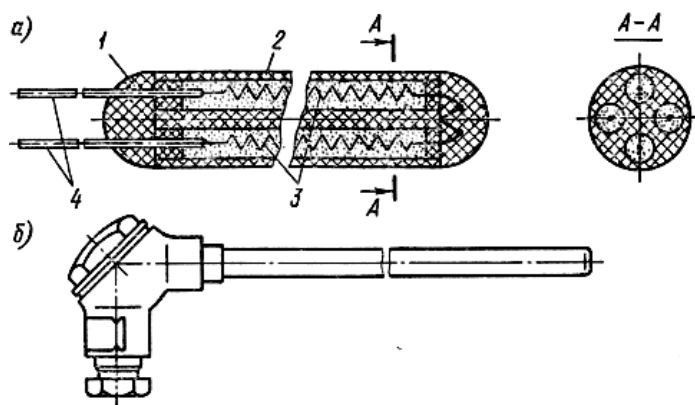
Устройство и внешний вид защитного корпуса платинового термометра сопротивления
